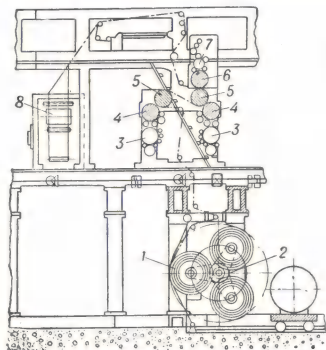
Схема секции ротац. газетного агрегата ГА: 1 — рулон бумаги; 2 — ролевая звезда; 3 — основные красочные аппараты; 4 — формные цилиндры; 5 — печатные цилиндры; 6 — формный цилиндр второй краски; 7 — красочный аппарат второй краски; 8 — фальцевальный аппарат. Пунктиром показан путь бумажного полотна.
